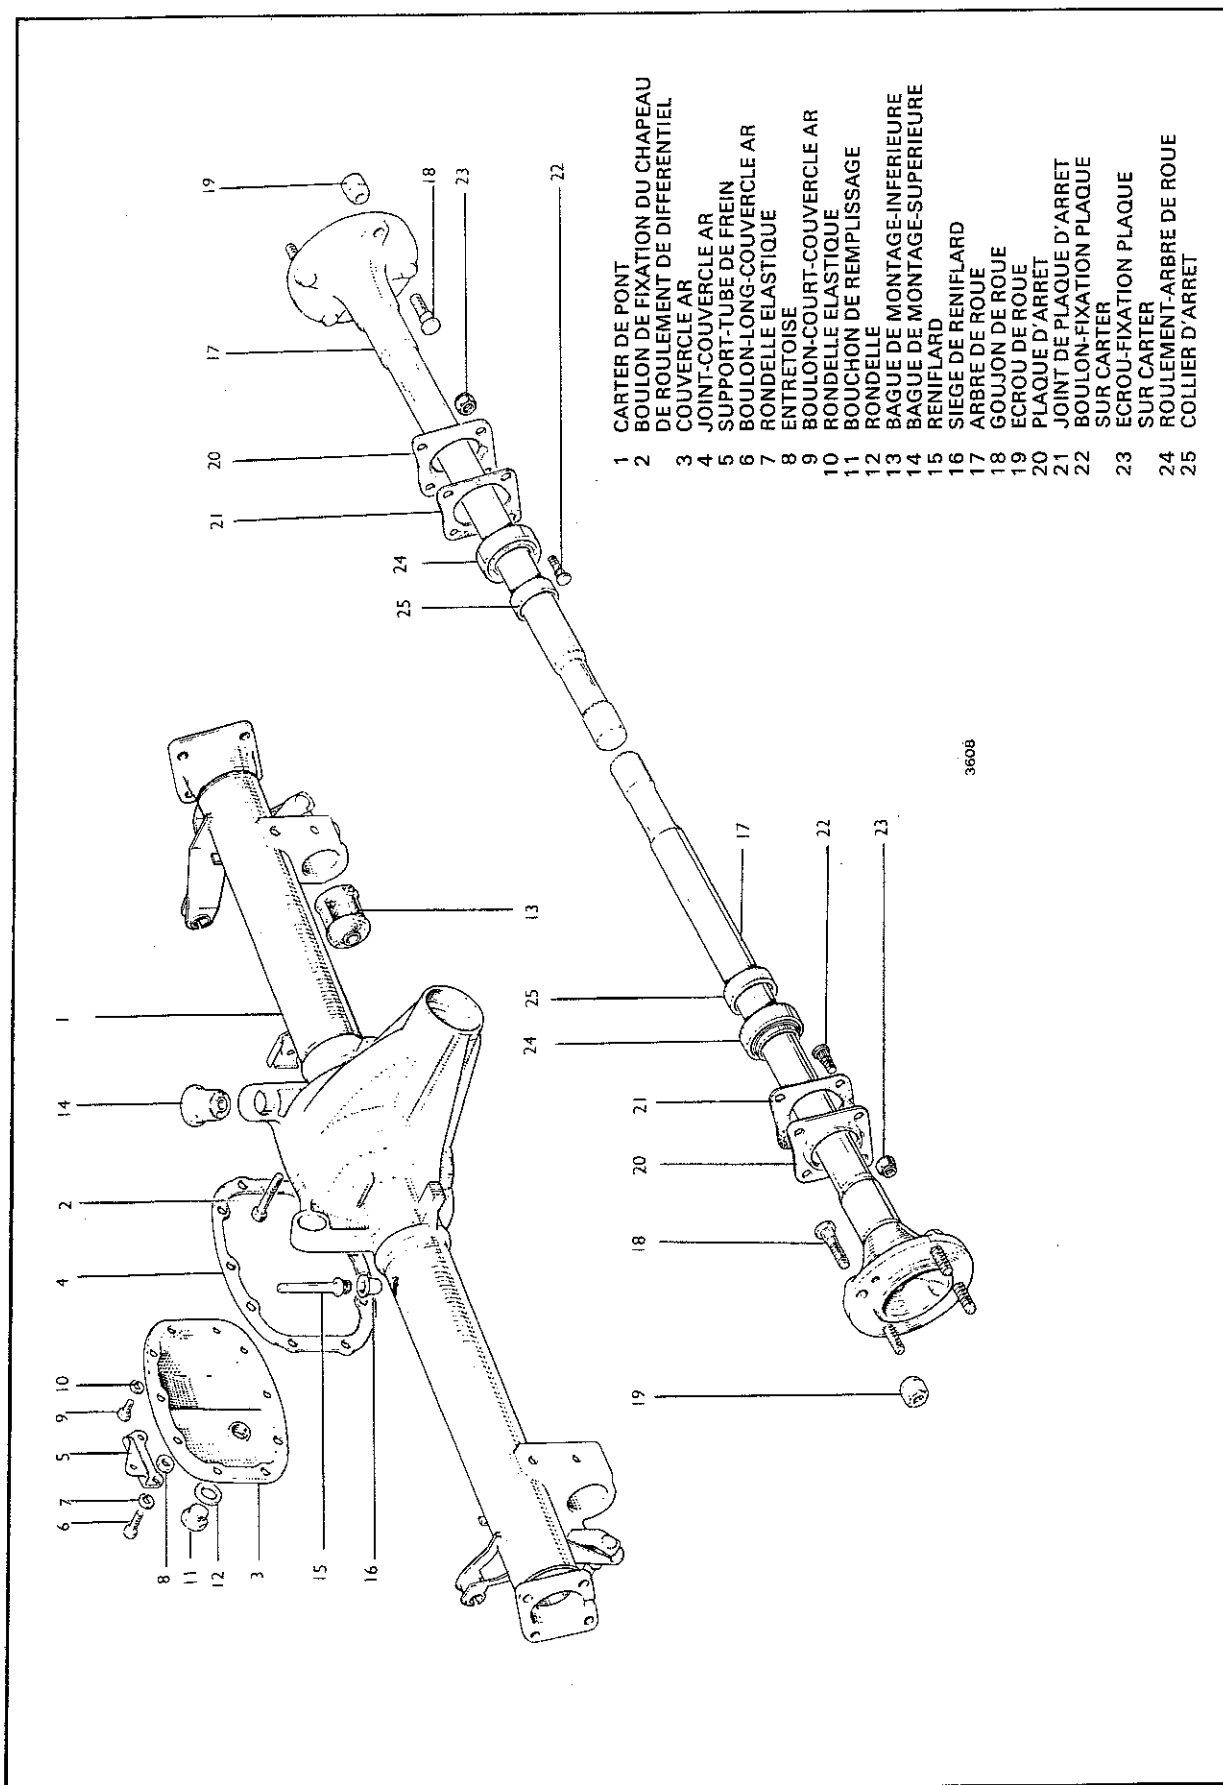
Vue éclatée de l'ensemble de pont AR.
